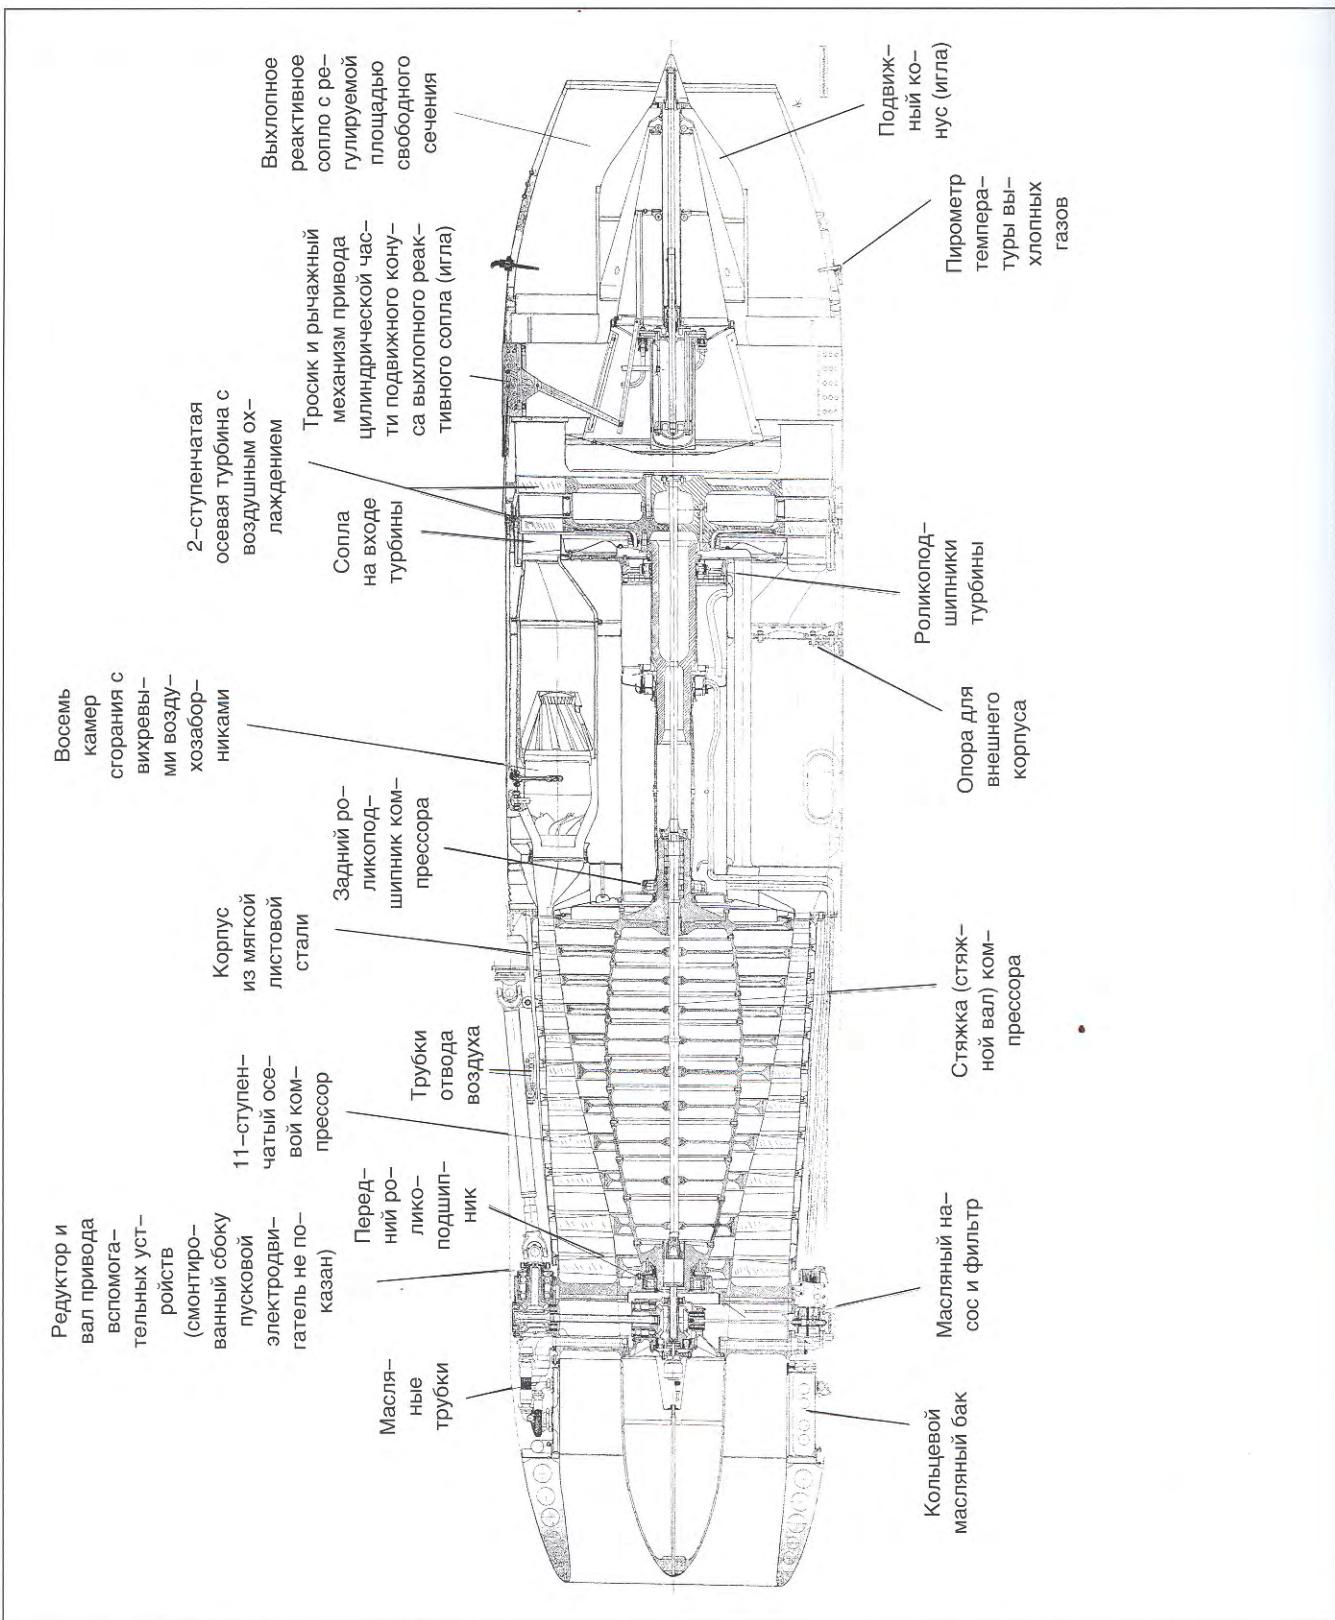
Устройство турбореактивного двигателя Юнкерс 109-012 А, класс III. Данный общий чертеж подготовлен на основе чертежей фирмы Junkers, выполненных в апреле 1944 года, однако в обобщенном виде он так и не появился до конца войны
